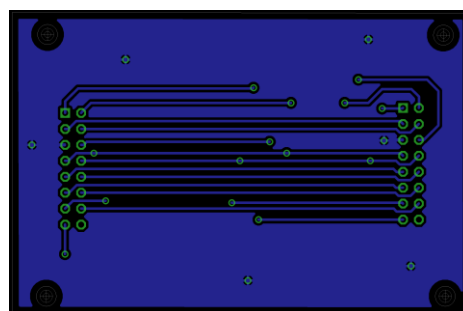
SCHEDA BUFFER PA BOTTOM
